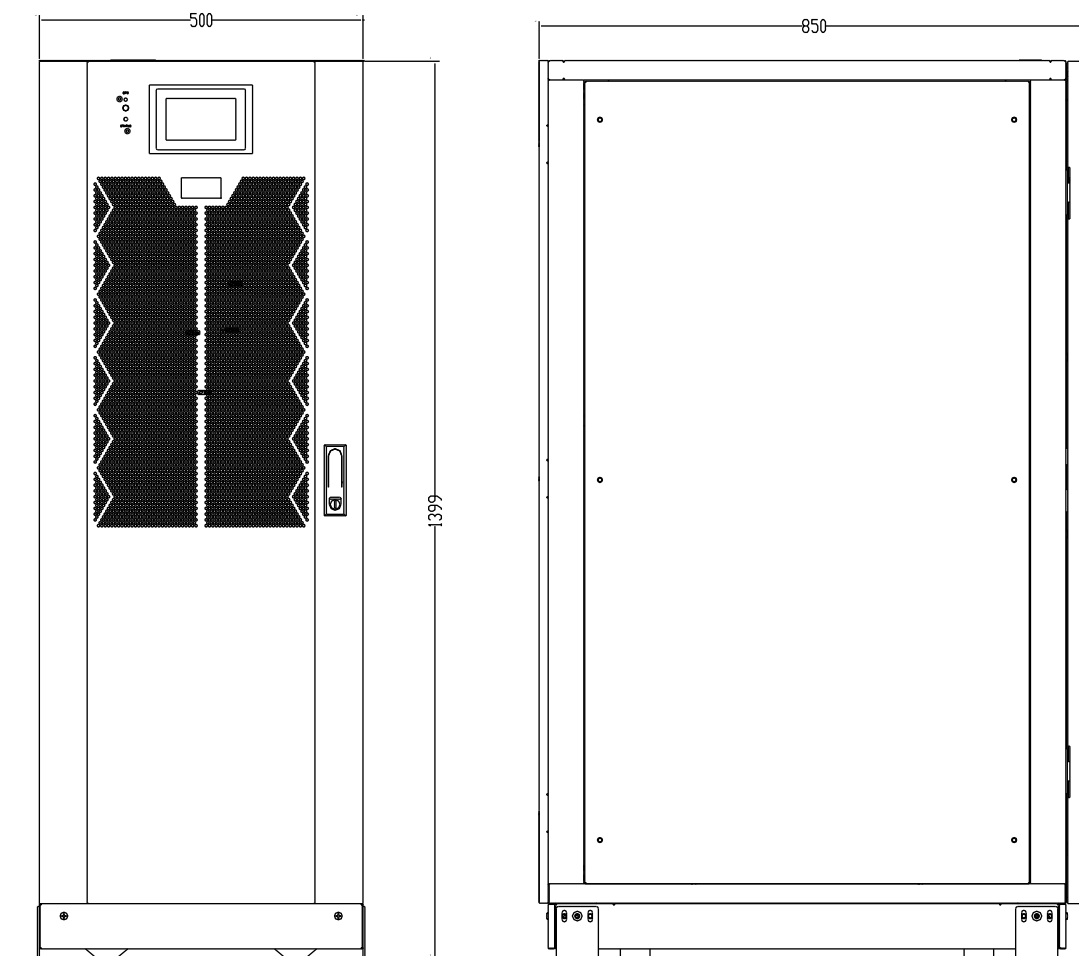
Размеры ИБП 40kVA (увеличенный типоразмер)
